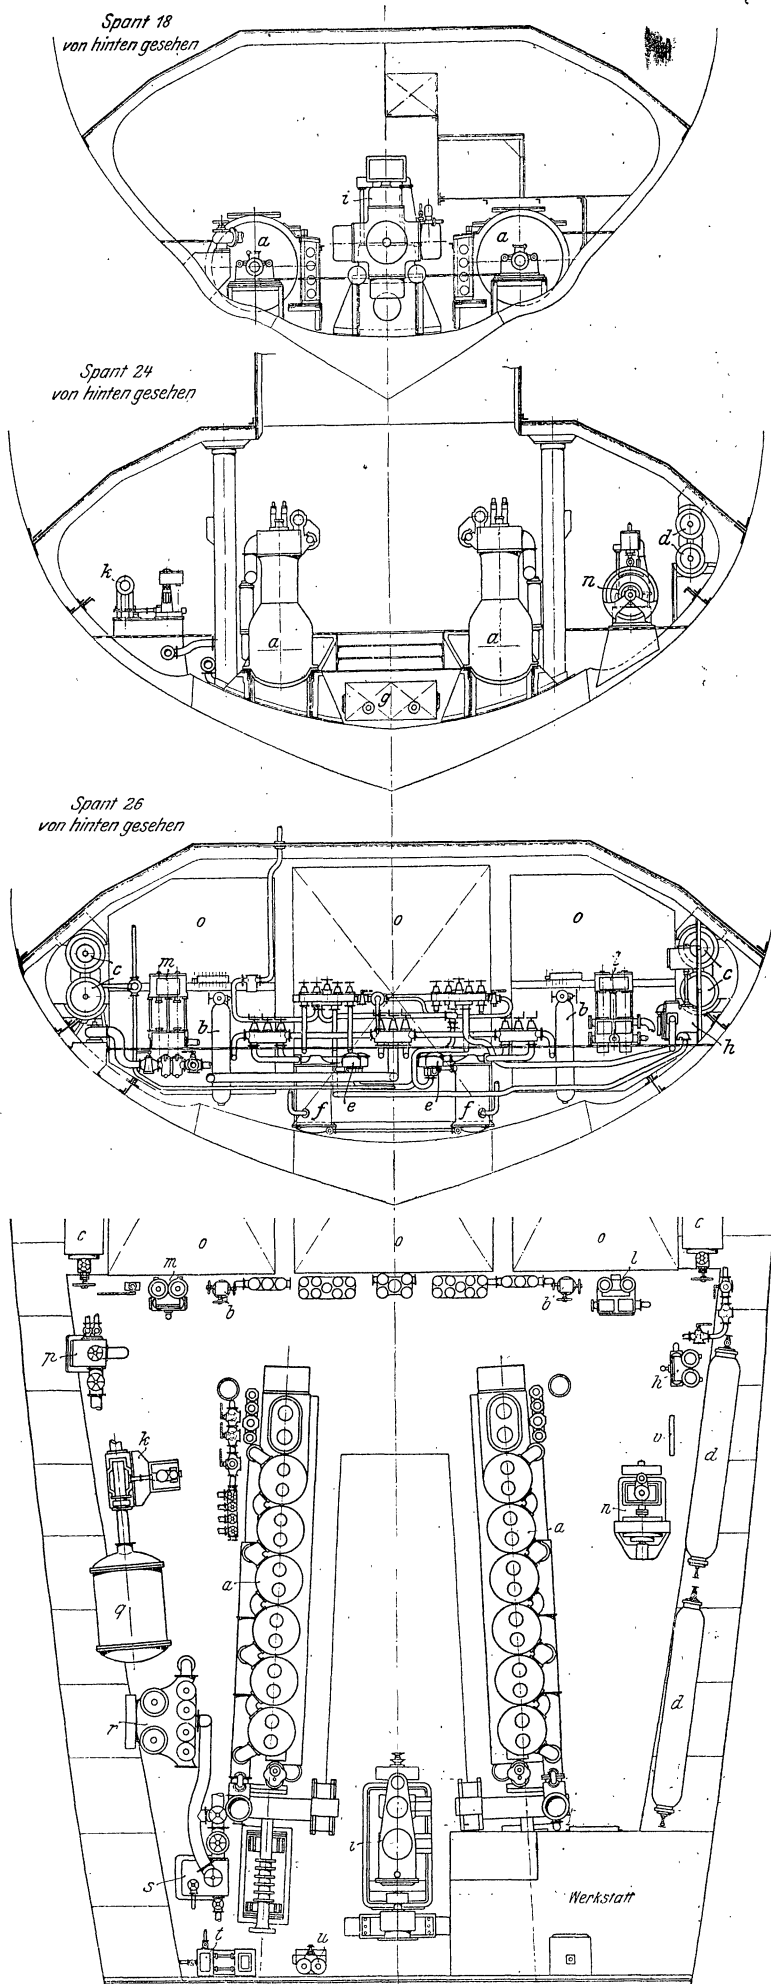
bis 9. Querschnitte und Grundriß des Maschinenraumes.
